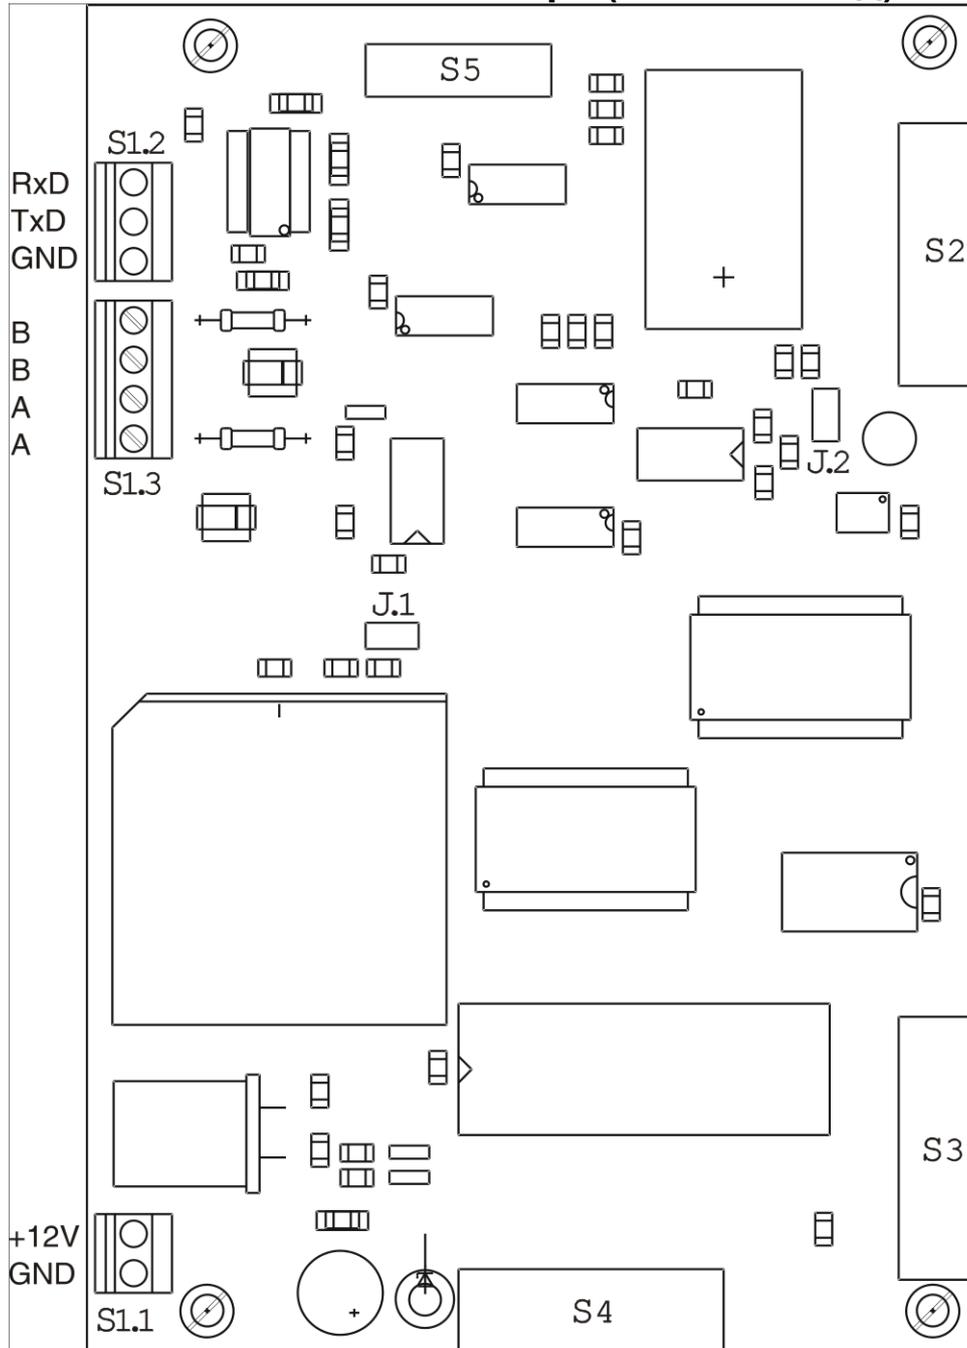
Внешний вид печатной платы Main-12002K в сборе
